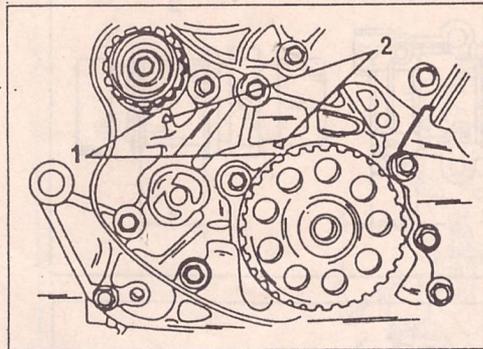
Установка малого зубчатого ремня и натяжного ролика
